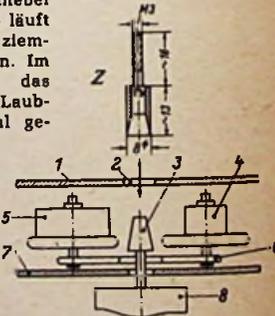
Seltensicht des Getriebes. Z = Zwischenstück, 1 = obere Deckplatte, 2 = 10-mm-Bohrung, 3 = Motorkegel (Achsstumpf), 4 = Zwischenrad für 33 U/min, 5 = Zwischenrad für 78 U/min, 6 = Schwankplatte für Drehzahl-schaltung, 7 = Montageplatte, 8 = Motor. Drehzahl-schaltung: Schwankplatte 6 nach links = 33, nach rechts = 78 U/min. Gezeichnete Stellung = Mittelstellung.
